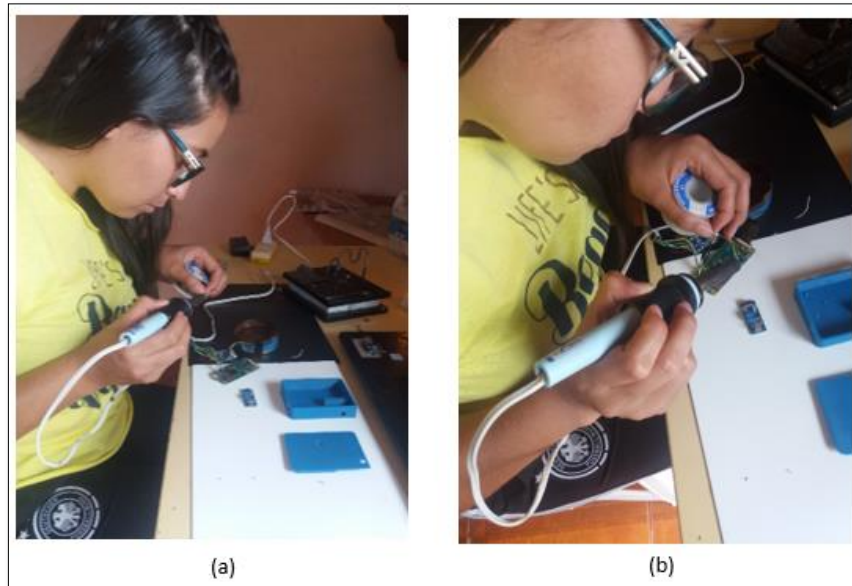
(a) y (b) Soldadura de elementos electrónicos.
